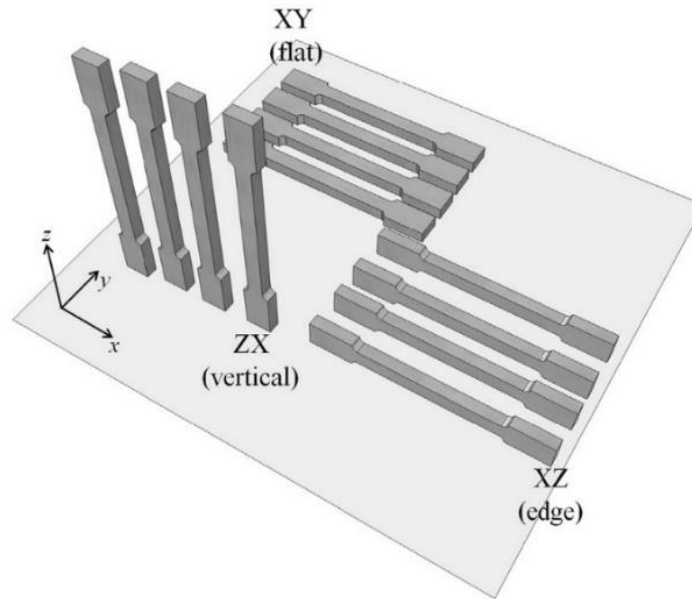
Modelos de probetas para ensayos de tracción. Construido en tres orientaciones distintas (vertical, de costado y plano) por proceso SLM [25]
